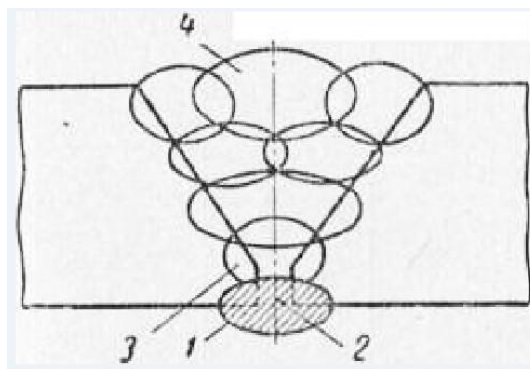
Сечение V-образного шва: 1-контрольный (подварочный) валик; 2-контрольная канавка; 3-первый слой; 4-усиление.
